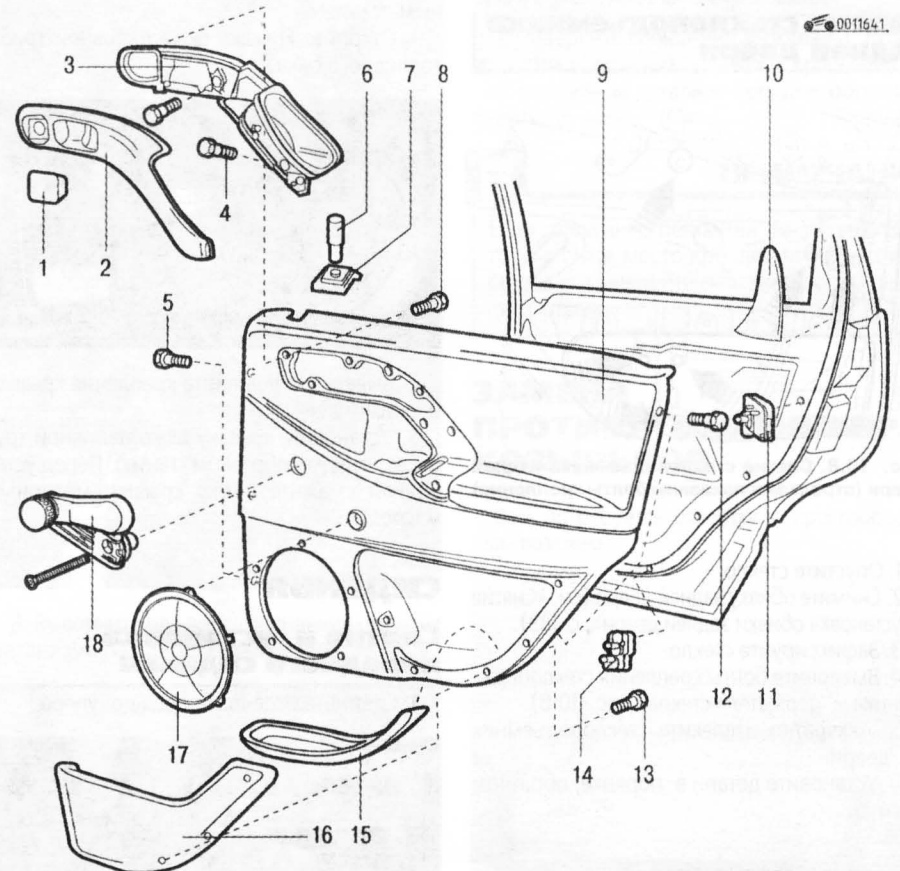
Детали обивки задней двери: 1 – заглушка; 2 – декоративная накладка дверной ручки; 3 – дверная ручка; 4, 5, 8, 12, 13 – винты; 6 – кнопка блокировки дверного замка; 7 – направляющая кнопки блокировки замка; 9 – обивка двери; 10 – декоративная накладка; 11, 14 – скобы; 15 – резиновая отделка; 16 – карман; 17 – решетка динамика аудиосистемы; 18 – ручка стеклоподъемника
